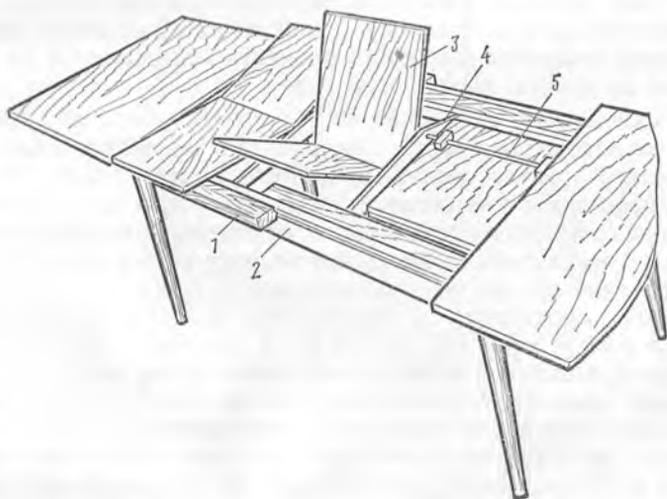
Конструкция стола с раздвижными крышками и нераздвижной круглой царгой:
